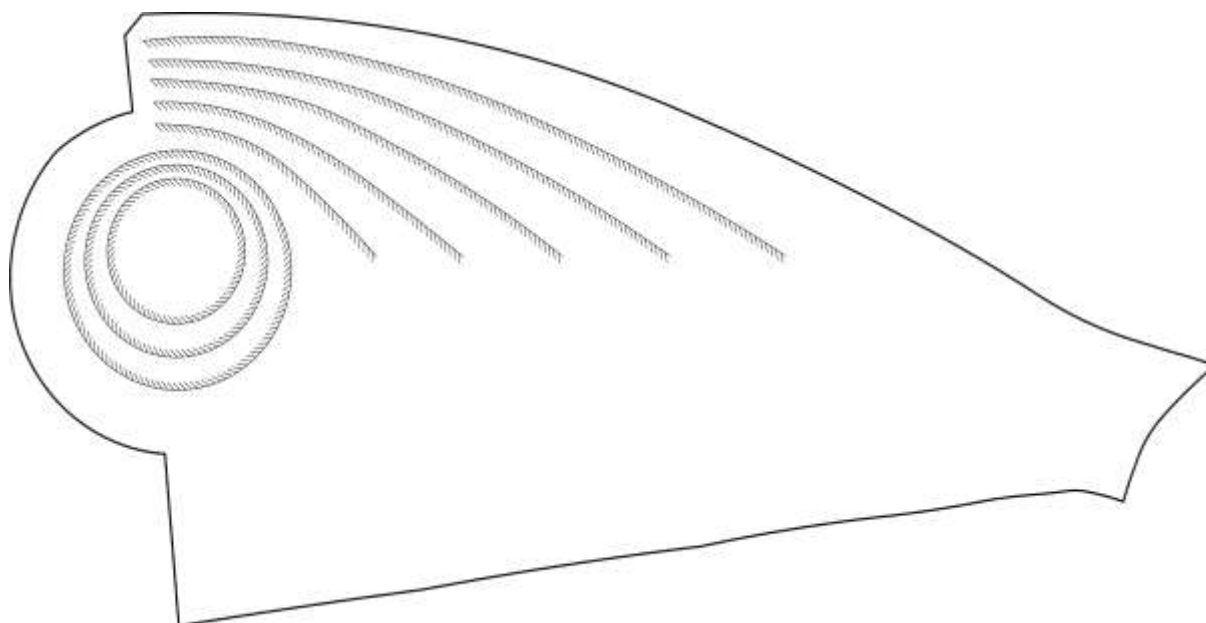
Деталь заготовки верха обуви с ажурной строчкой «гладьевой валик»
